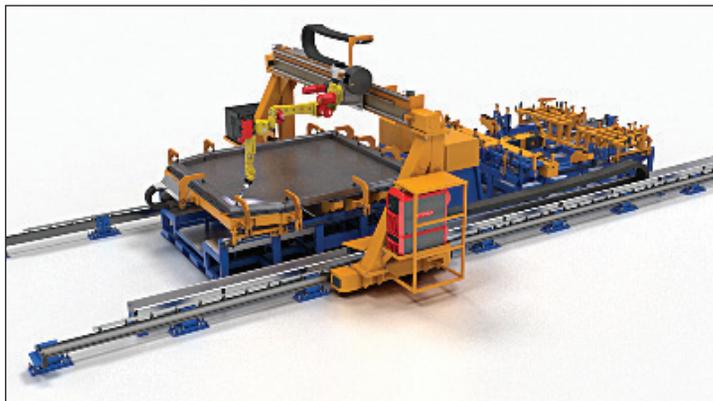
Роботизированный комплекс сборки и сварки задних дверей самосвала
